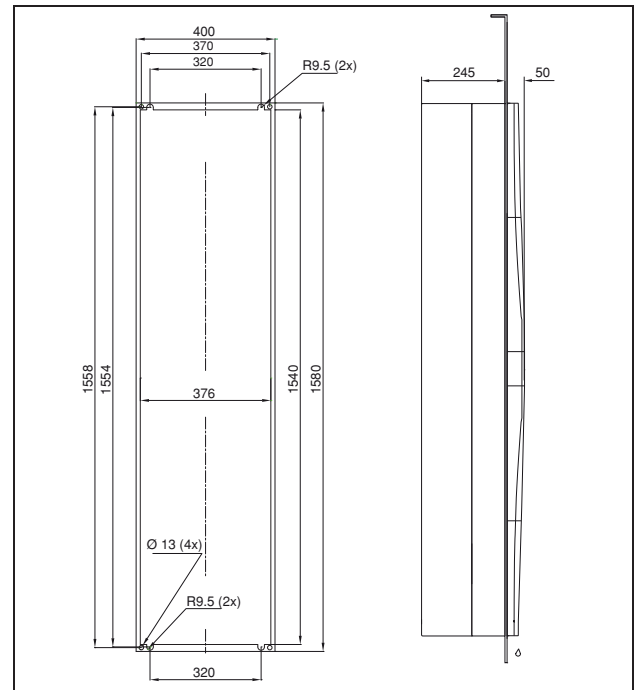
3328.xxx, 3329.xxx komplett inbyggnad
